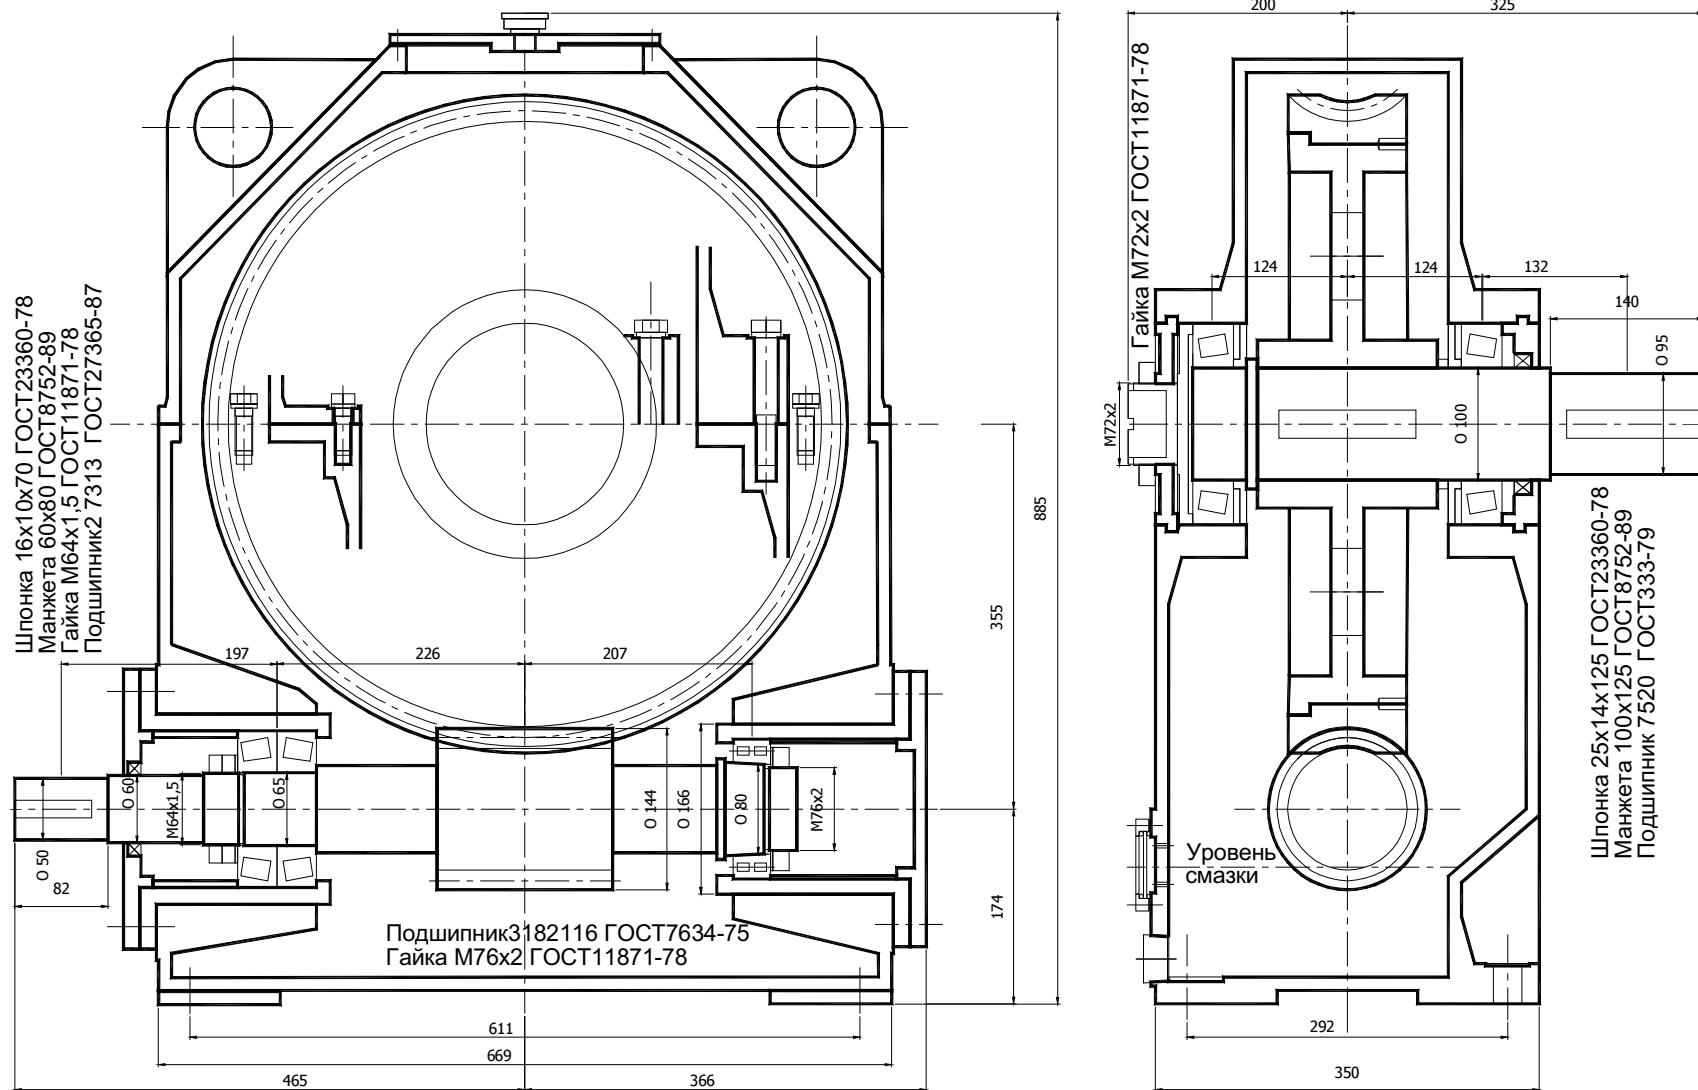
Компоновка редуктора с горизонтальными валами и нижним расположением червяка
